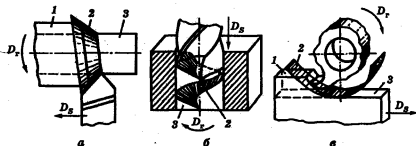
Поверхности обработки при точении (а), сверлении (б), цилиндрическом фрезеровании (в):
